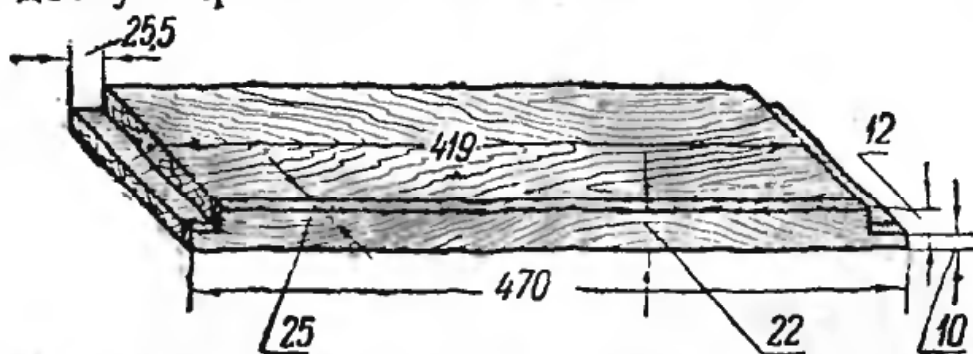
Разметка и обработка заготовки № 25 для верхних брусков.
